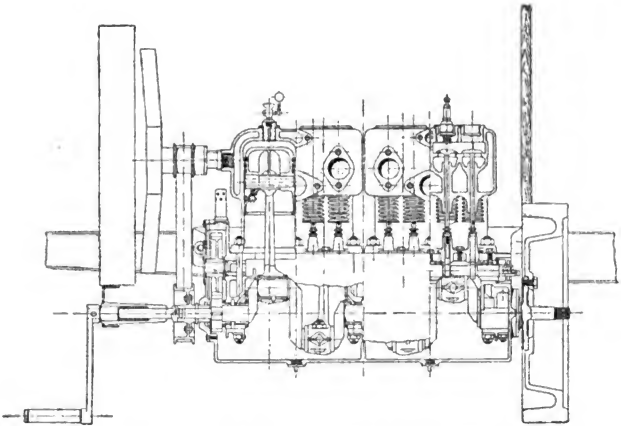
Dixi-Motor der Fahrzeugfabrik Eisenach.
